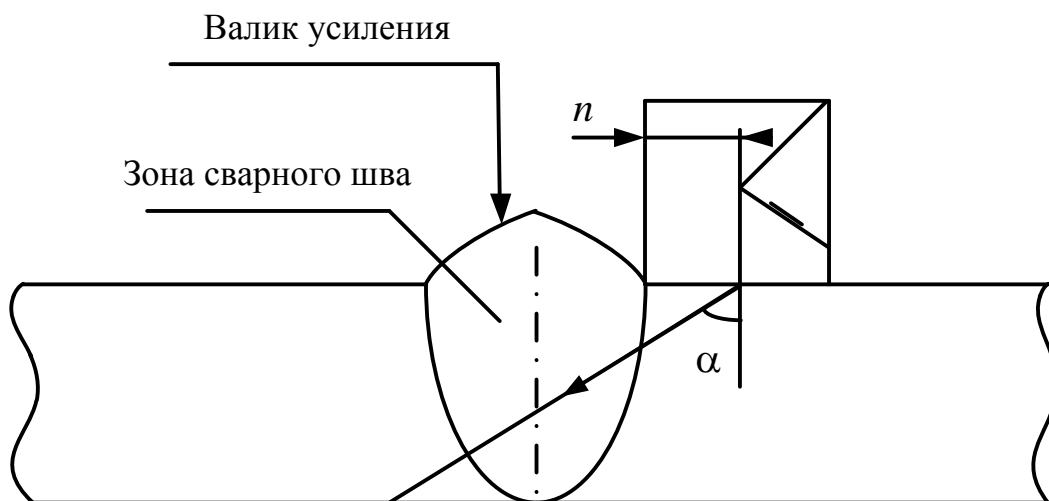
Расположение ПЭП при контроле сварного шва
